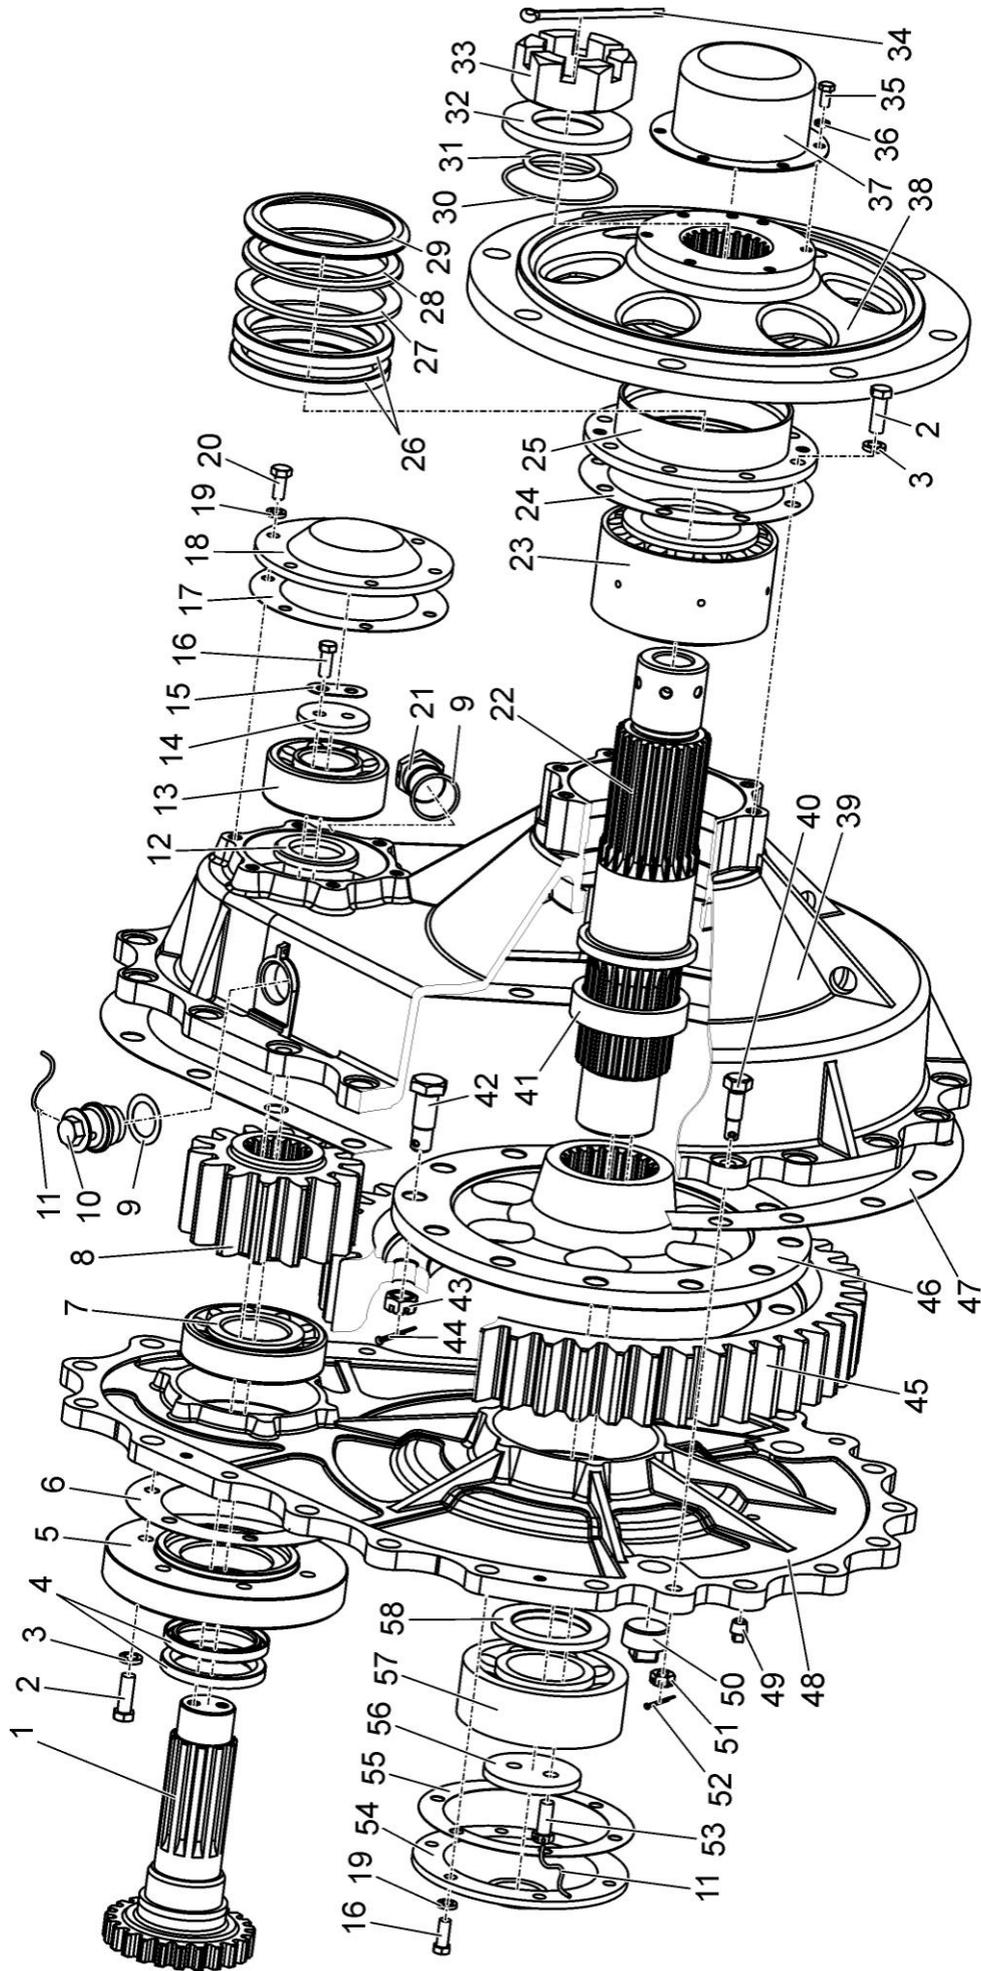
Передача конечная. Крышка. Шестерня ведомая
